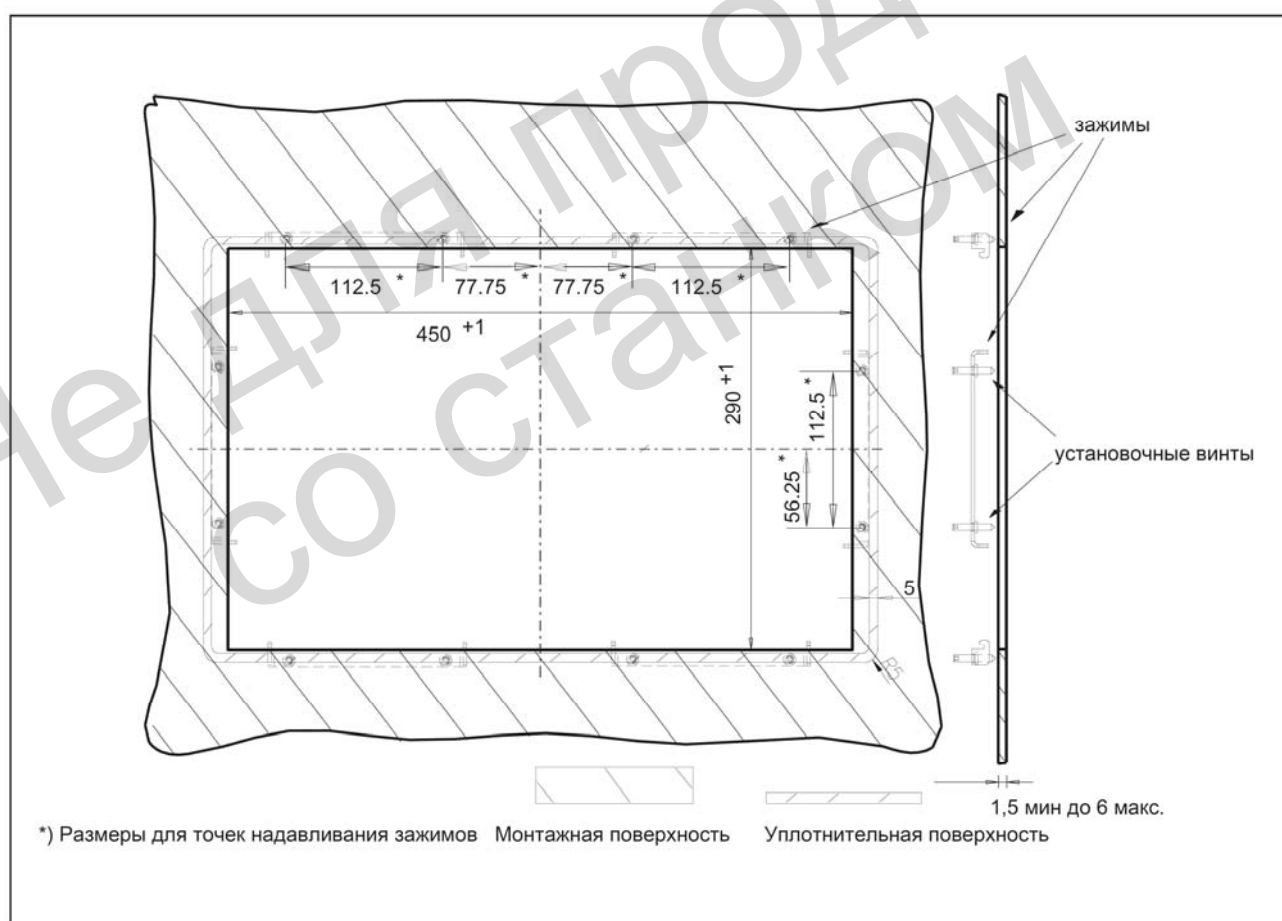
Габаритный чертеж для монтажа панели оператора OP 010
